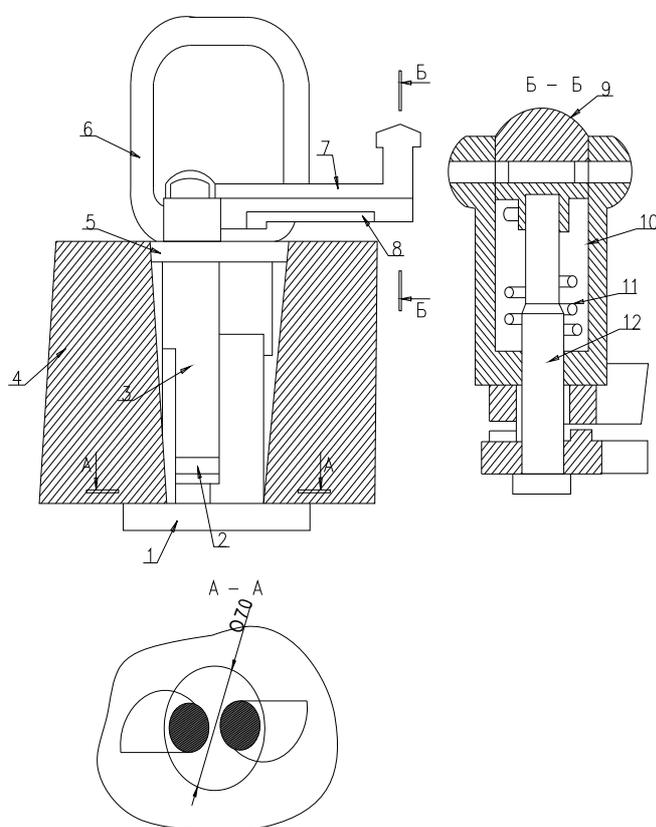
Двухрамочный захват конструкции ЦНИИОМТП для строповки колонн
